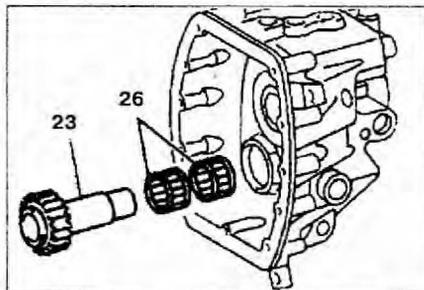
Снимите ведущий вал 23 и игольчатый подшипник 26 из корпуса коробки передач 31. Выпрессуйте через отверстие в корпусе коробки передач крышку 15, используя пробойник.
